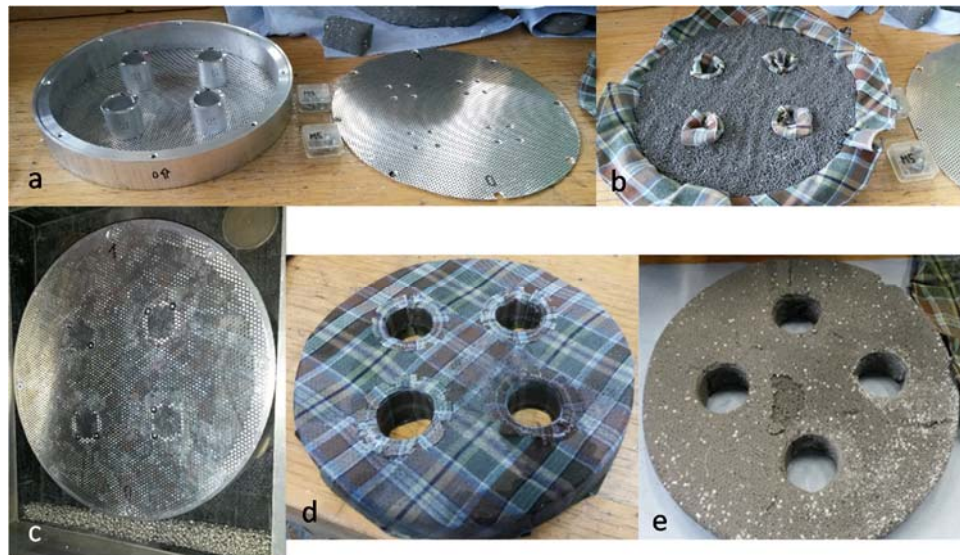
Einlegerwerkzeug der zweiten Generation für KSB-Ringe. a) Werkzeug aus Aluminiumlegierungen, b) befüllt mit Grünkugeln und textiler Trennung (100 % Baumwolle), c) gefülltes Einlegerwerkzeug in der Schäumkammer des FTA, d) Trocknung des Formkörpers in der textilen Hülle, e) nach Entfernung der textilen Hülle.
